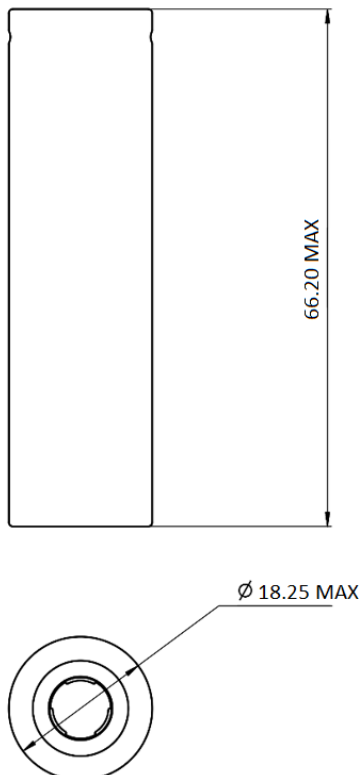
Габаритные размеры LTO18650-1500CC
